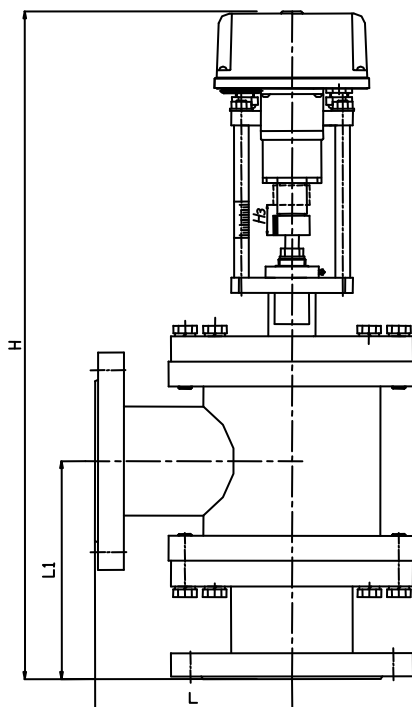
Габаритные установочные и присоединительные размеры клапана.
